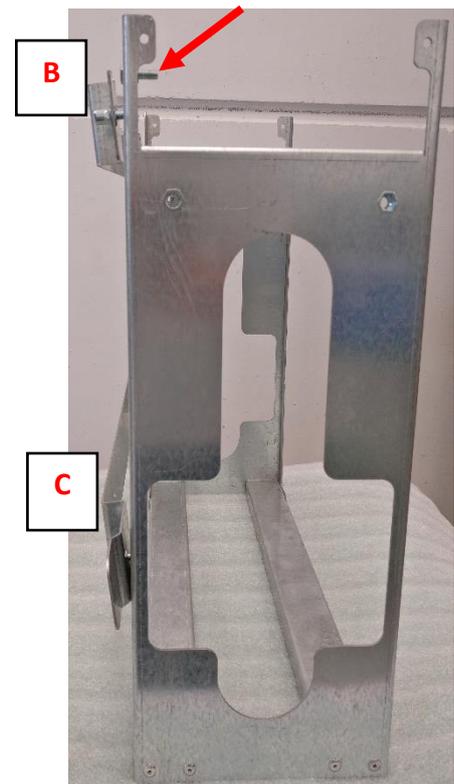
Instalación de las abrazaderas en la caja de baterías: respete la dirección de la instalación
